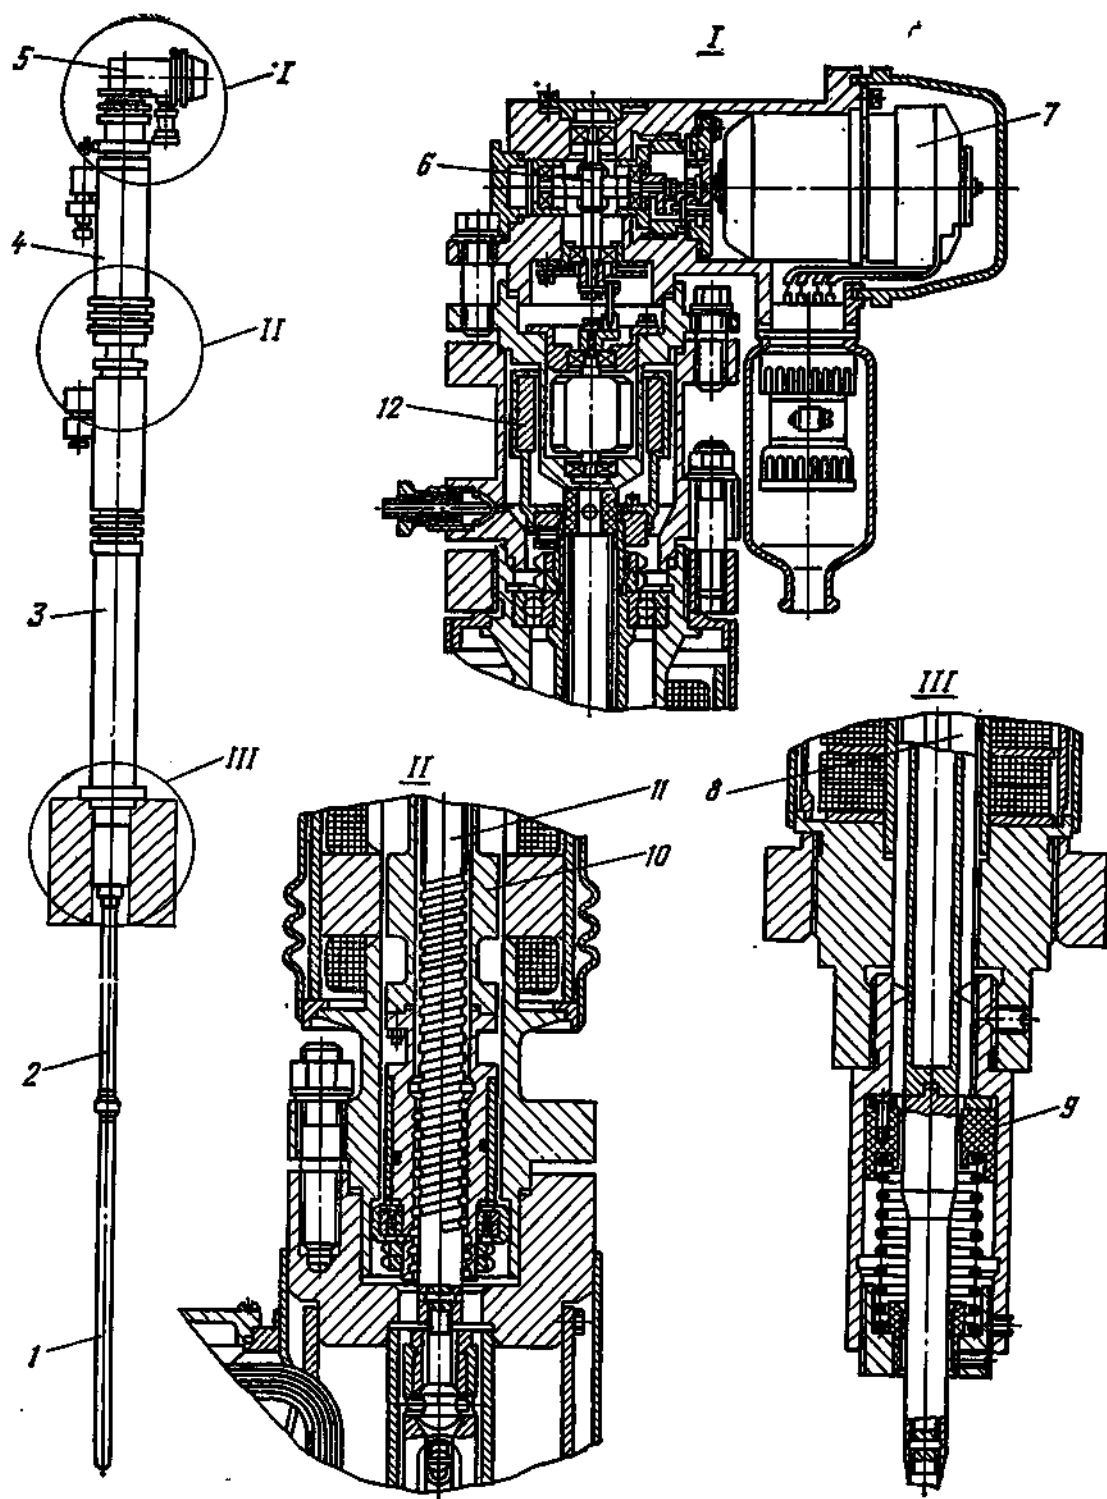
Исполнительный механизм СУЗ реактора СМ-2
